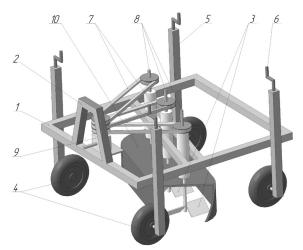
Ботвоудаляющая машина: 1 — рама; 2 — устройство для присоединения к трактору; 3 — рабочие органы; 4 — пневматические колеса; 5 — стойки; 6 — механизм механического регулирования высоты скашивания; 7 — ременные передачи; 8 — валы; 9 — конический редуктор; 10 — кожух
